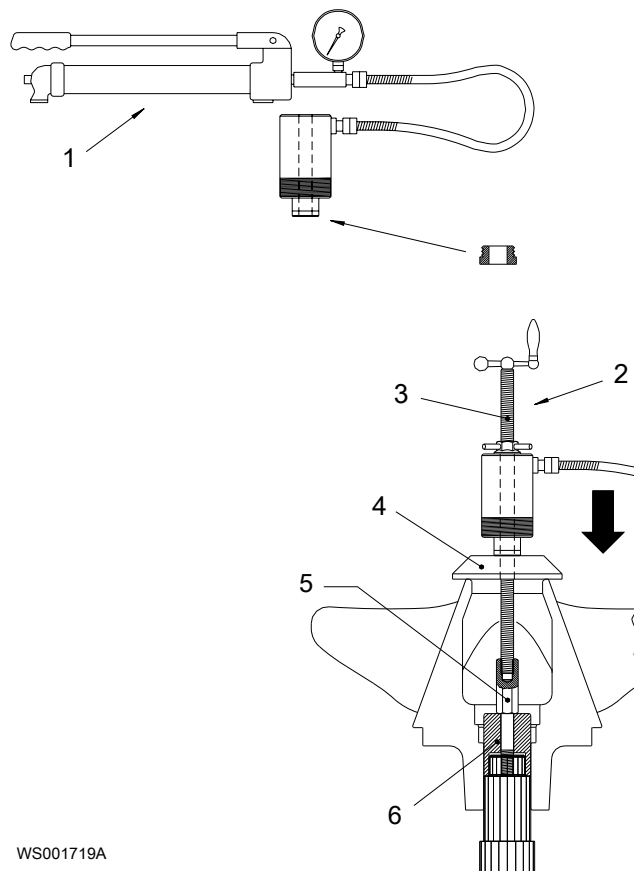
Установка гидравлического инструмента и резьбового стержня.
